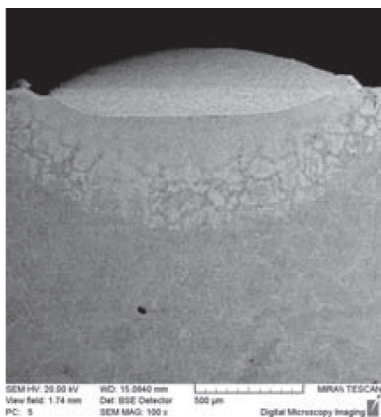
Поперечный шлиф валика, полученного лазерной наплавкой сплава ПГ-12Н-01 при скорости наплавки  $V = 40$  мм/мин и дистанции наплавки  $L = 10$  мм
